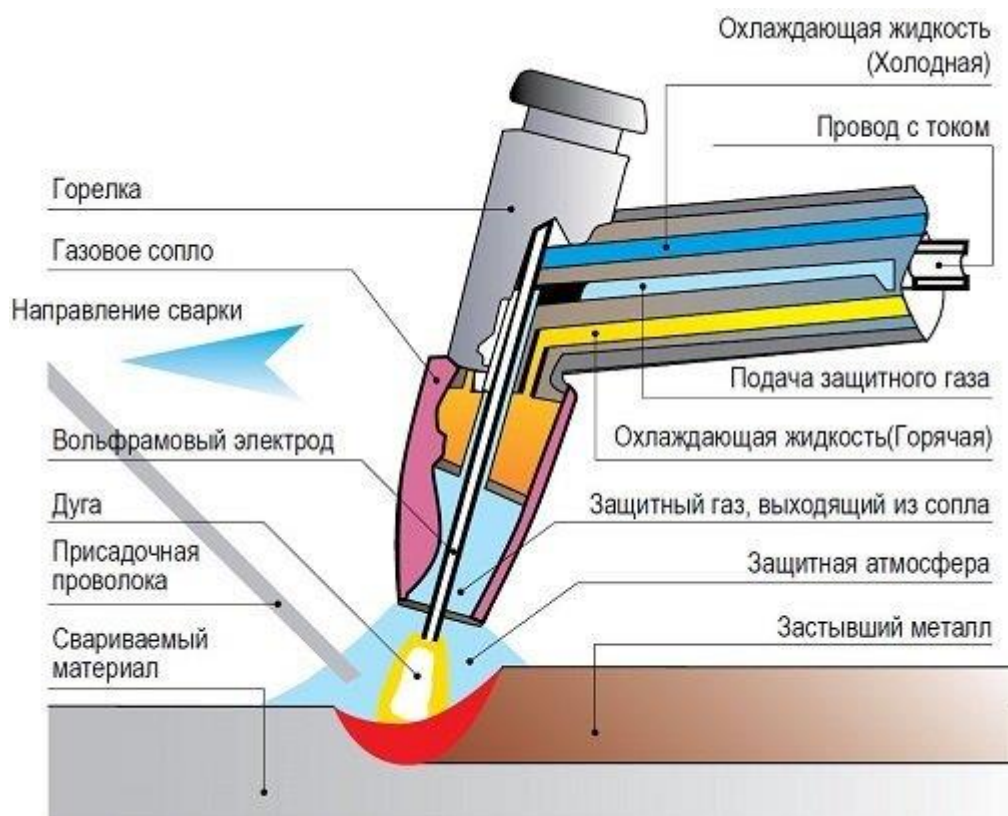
Принцип работы аргонодуговой сварки.
